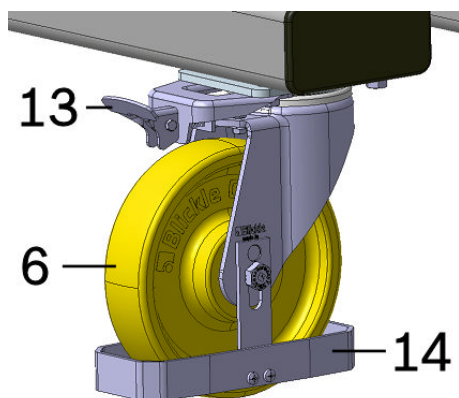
Самоустанавливающееся колесо, детальный вид
